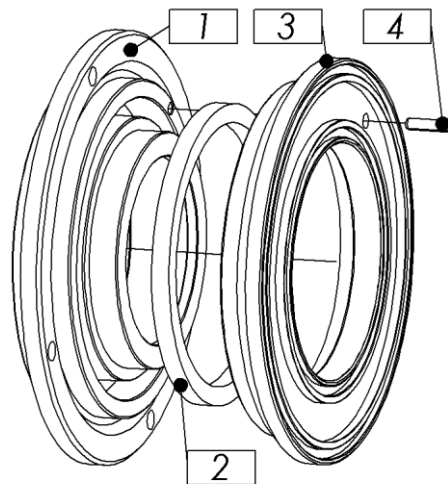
806.04.40.A – Axial-Zylinder komplett
